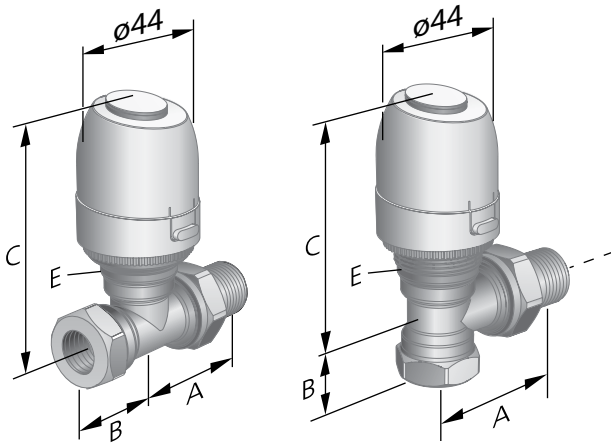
Клапан VALVE-S (прямой) и VALVE-A (угловой) с приводом ACTUATOR.
